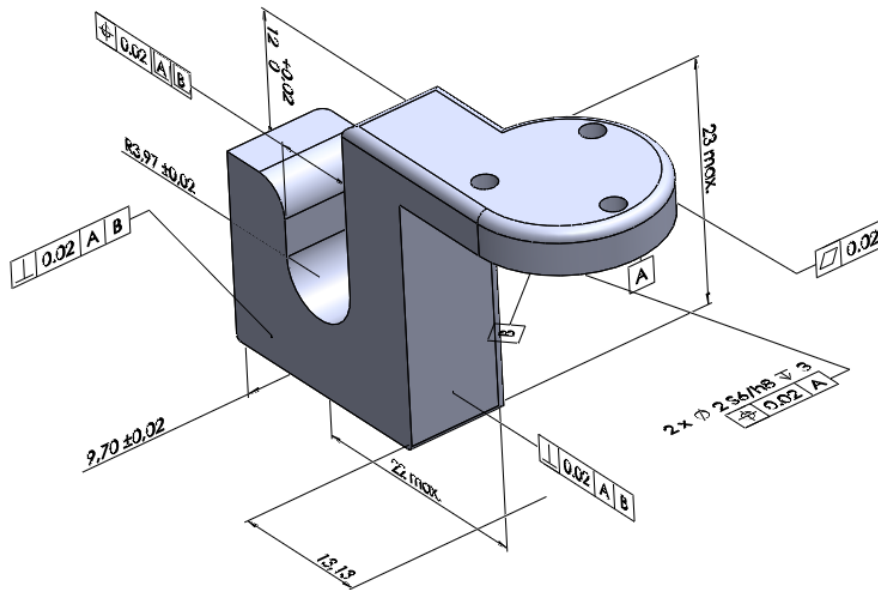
Zadane dimenzijske i geometrijske tolerancije Fiksne čeljusti klizača prednjeg uležištenja
